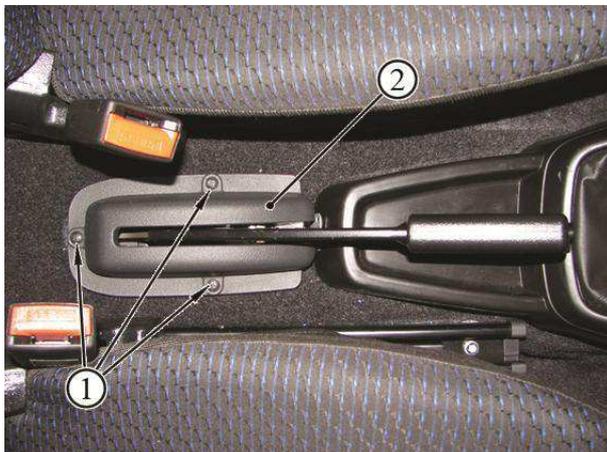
Крепление защитного чехла стояночного тормоза:
